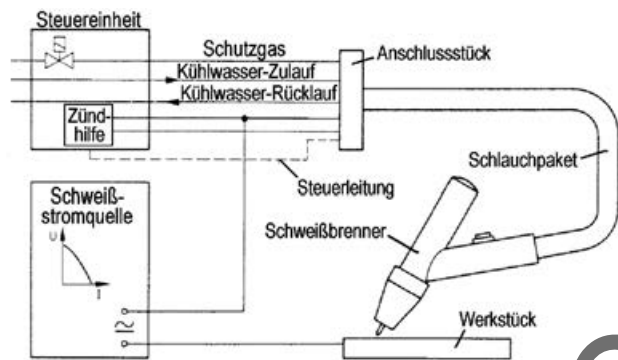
WIG-Schweißeinrichtung, schematisch.
